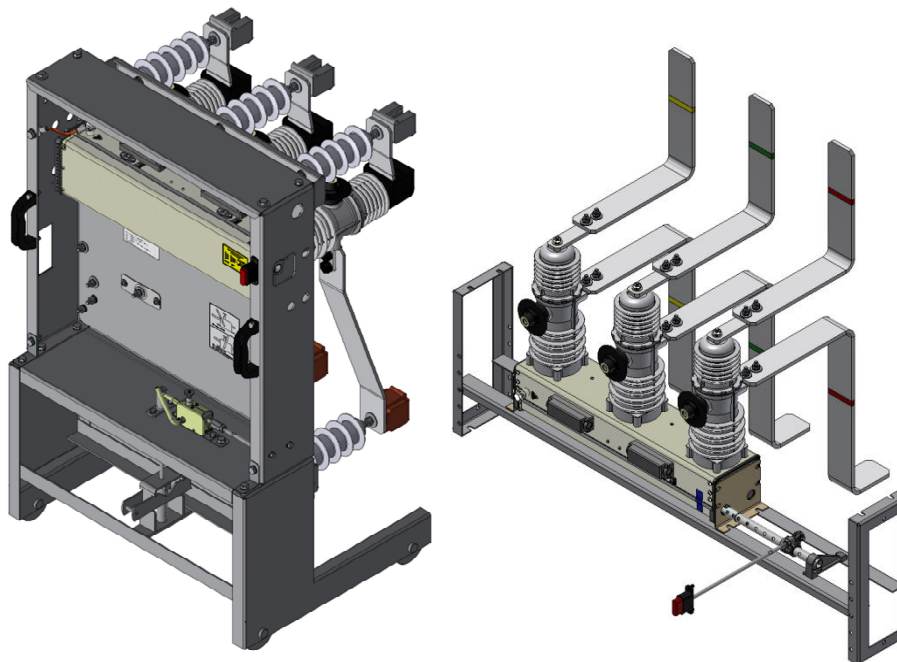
Общий вид выключателя TER_VCB25_LD1_RF
